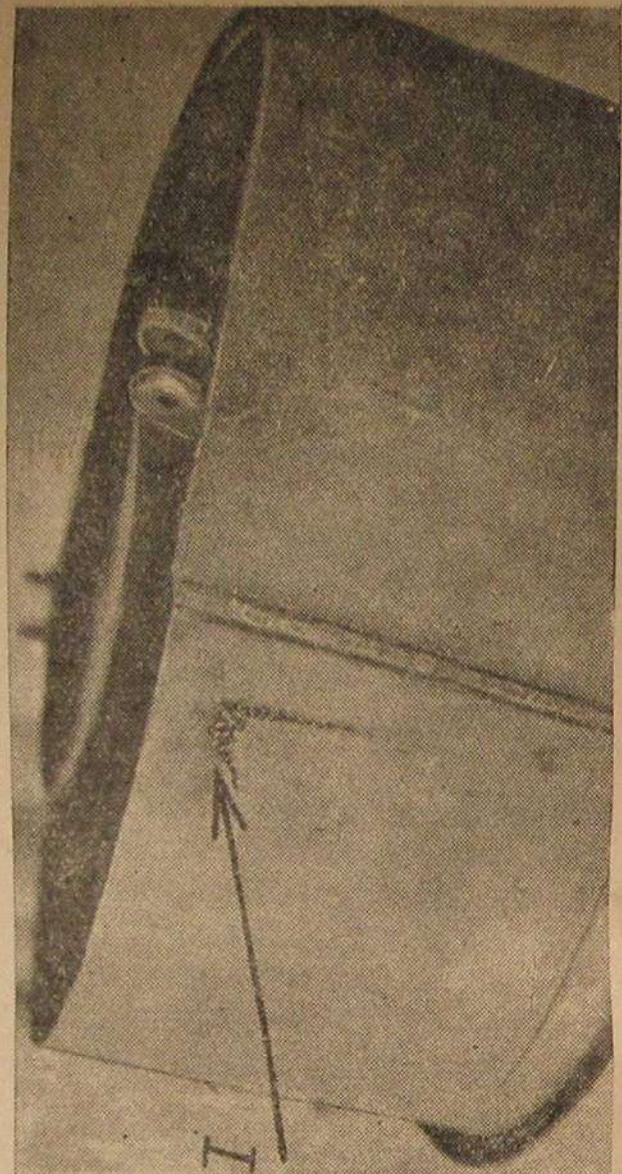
Верхний наружный кожух, разъединенный конденсатом.
